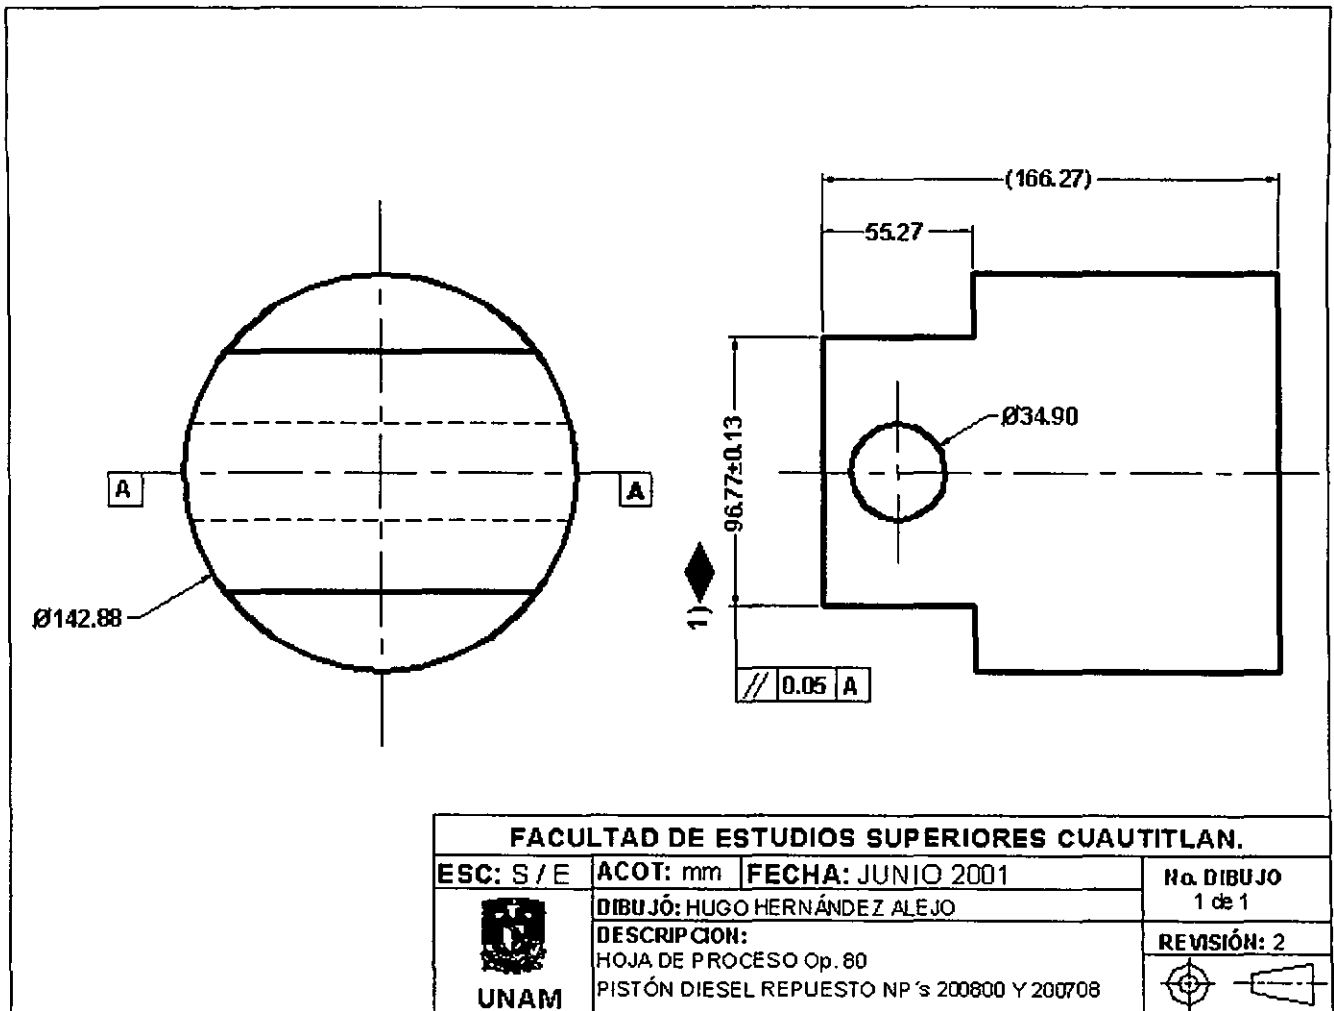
Hoja de proceso para el maquinado de la falda del pistón.
